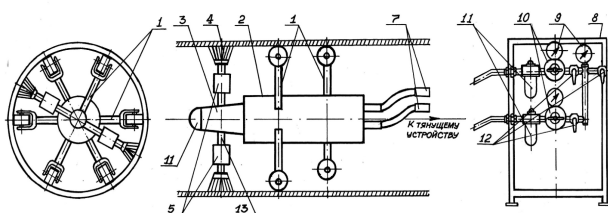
Схема установки очистки внутренней поверхности трубы металлическими щетками
